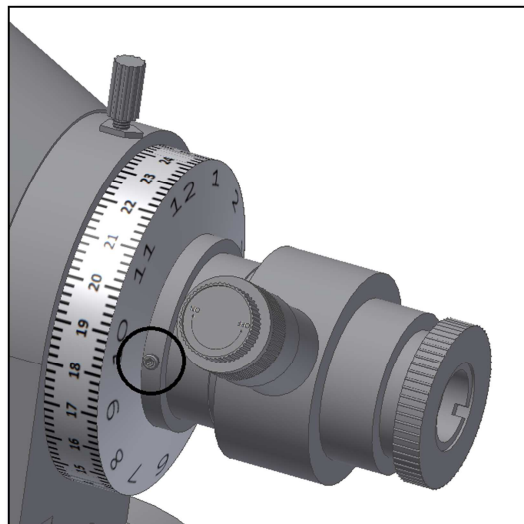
Lösen Sie die Sechskantschrauben, um den Ring drehen zu können.
